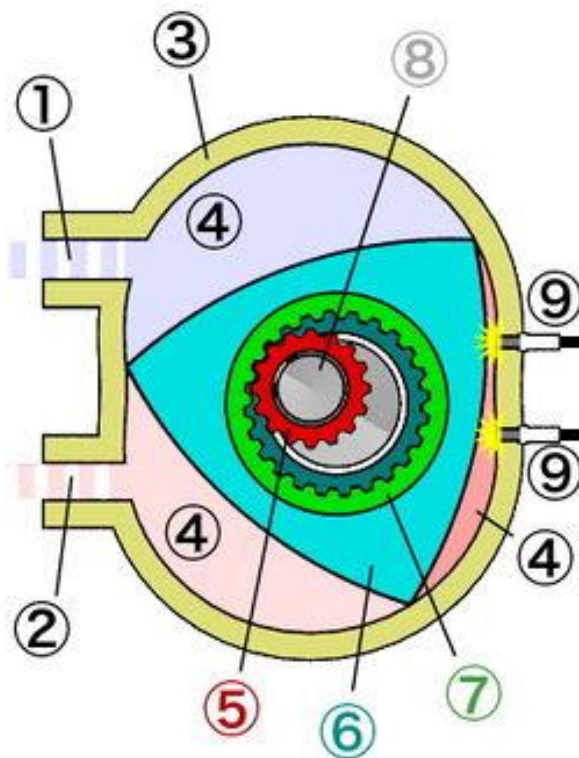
Схема роторно-поршневого двигуна Ванкеля [24]:
